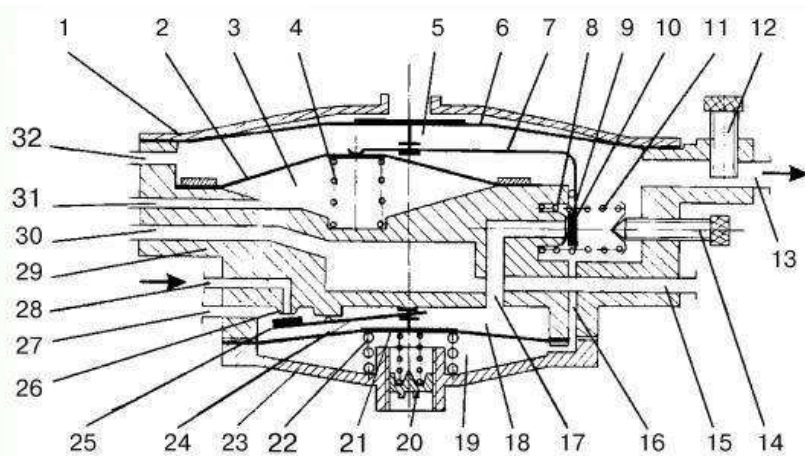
Схема редуктора-испарителя «САГА-6»: 1 – крышка второй ступени; 2 – диафрагма разгрузочного устройства; 3 – полость разгрузочного устройства; 4, 8, 11, 22 – пружины; 5 – полость второй ступени; 6 – диафрагма второй ступени; 7, 24 – рычаги; 9, 25 – клапаны; 10 – седло клапана второй ступени; 12 – дозатор; 13 – канал выхода газа; 14 – регулировочный винт холостого хода; 15, 30 – каналы соответственно подвода и отвода теплоносителя; 16 – канал обратной связи; 17 – канал, соединяющий полости высокого и низкого давления; 18 – полость первой ступени; 19 – подпружиненная полость первой ступени; 20 – винт регулировки давления первой ступени; 21 – диафрагма первой ступени; 23 – крышка первой ступени; 26 – седло клапана первой ступени; 27 – канал слива конденсата из полости первой ступени; 28 – канал подвода газа; 29 – корпус редуктора; 31 – канал для подсоединения к впускному трубопроводу двигателя или задрессельному пространству карбюратора; 32 – канал слива конденсата из полости второй ступени
